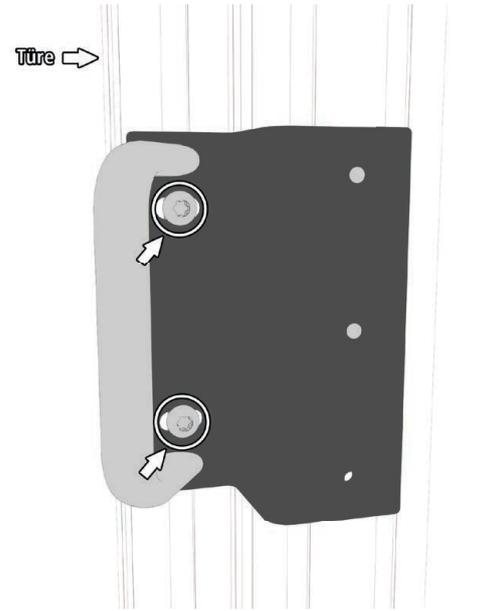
Montageplatte mit Ankerplatte am Profil anbringen und zur Prozesszuhalterung ausrichten. Schrauben M8 x 12 mm Torx festziehen.
